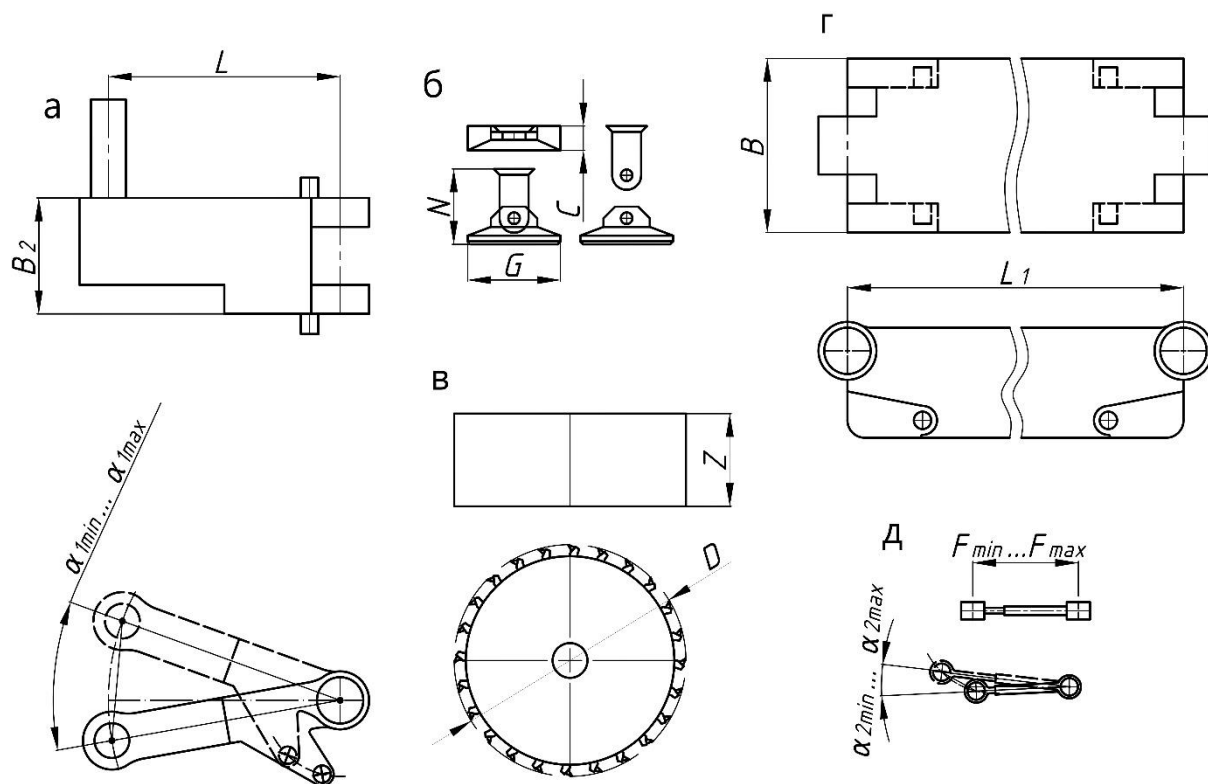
Составные элементы модели очистного комбайна: а –поворотный редуктор, б – лыжи, в – шнек, г – корпус, д – гидроцилиндр поворотного редуктора.
